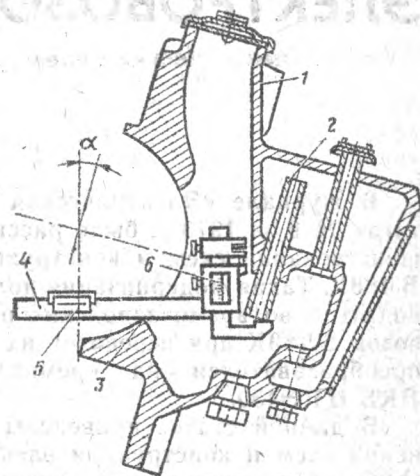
Проверка положения ниппеля относительно порожка шапки:
